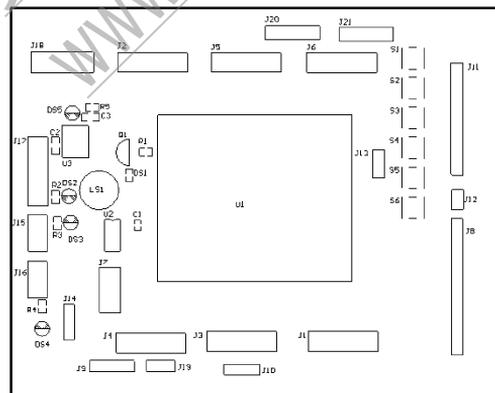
ATmega128 单片机 PACK 板接口控制板电路和 PCB 图
